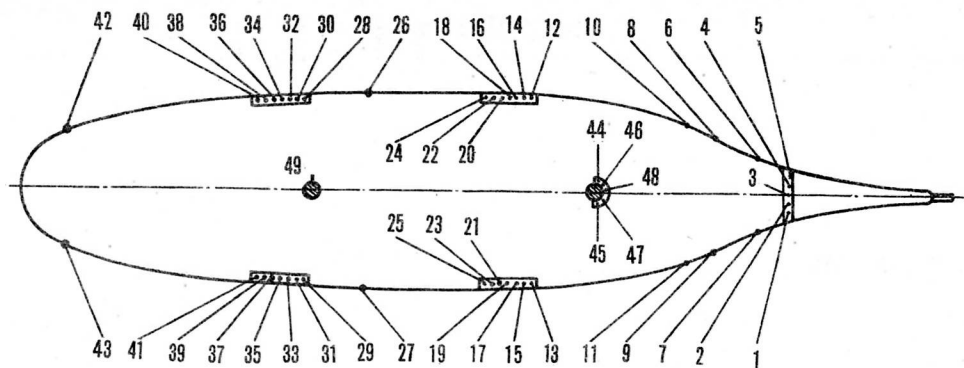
План крепления снастей двухмачтовой бермудской шхуны
